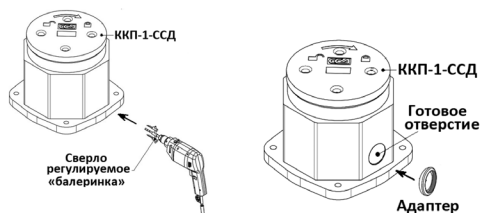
Сверление отверстия для адаптера гладкой трубы
